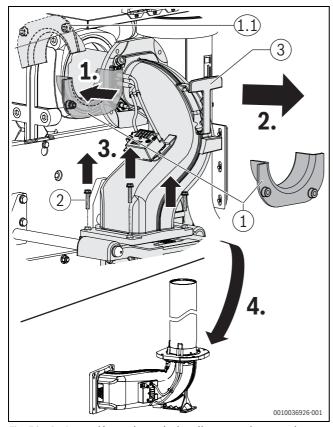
Retirer et déposer le coude de mélange avec la rampe de combustion
